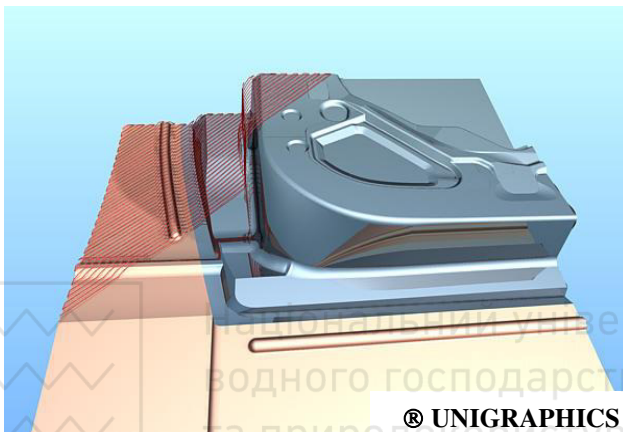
Моделювання процесу 3-осьової фрезерної обробки. в модулі UG/Fixed-Axis Milling
